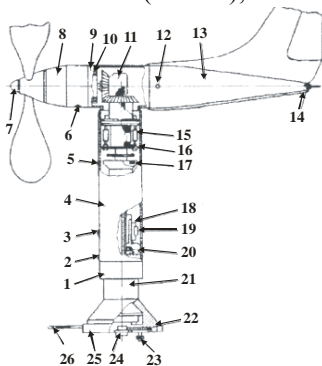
Датчик мгновенной скорости и направления ветра (М127) анеморумбометра М63М-1: 1 — втулка; 2, 3, 5 — винты; 4 — труба; 6 — стопорный винт; 7 — анкерный болт; 8 — корпус узла скорости; 9 — тройник; 10, 15–17, 20 — подшипники; 11 — шестерня с экраном; 12 — регулировочный болт; 13 — флюгарка; 14 — шпилька регулировочная; 18 — геркон; 19 — магнит; 21 — стопка; 22 — плата; 23 — болт; 24 — штепсельный разъем; 25 — кольцо; 26 — ориентир
